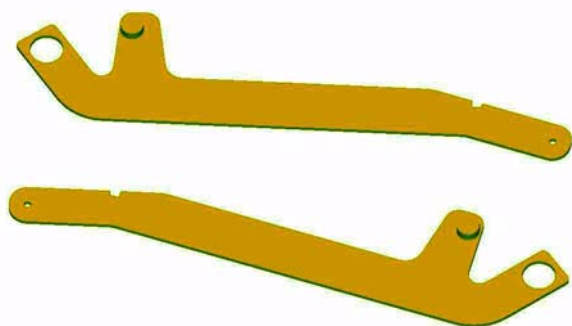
Скользящий рычаг для работы шторок, номер для заказа: 767-0103.3
